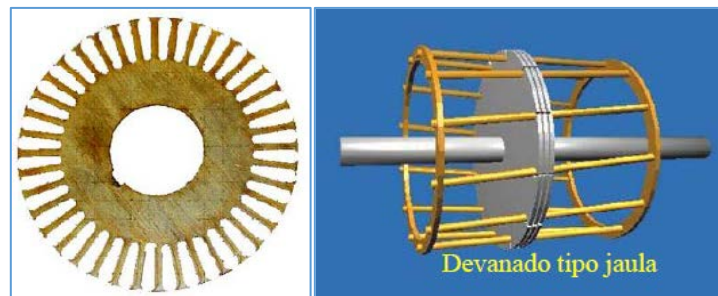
Chapa magnética del núcleo del rotor (a) y esquema de la jaula rotórica en un motor con rotor de jaula (b) [UPV 2012]
